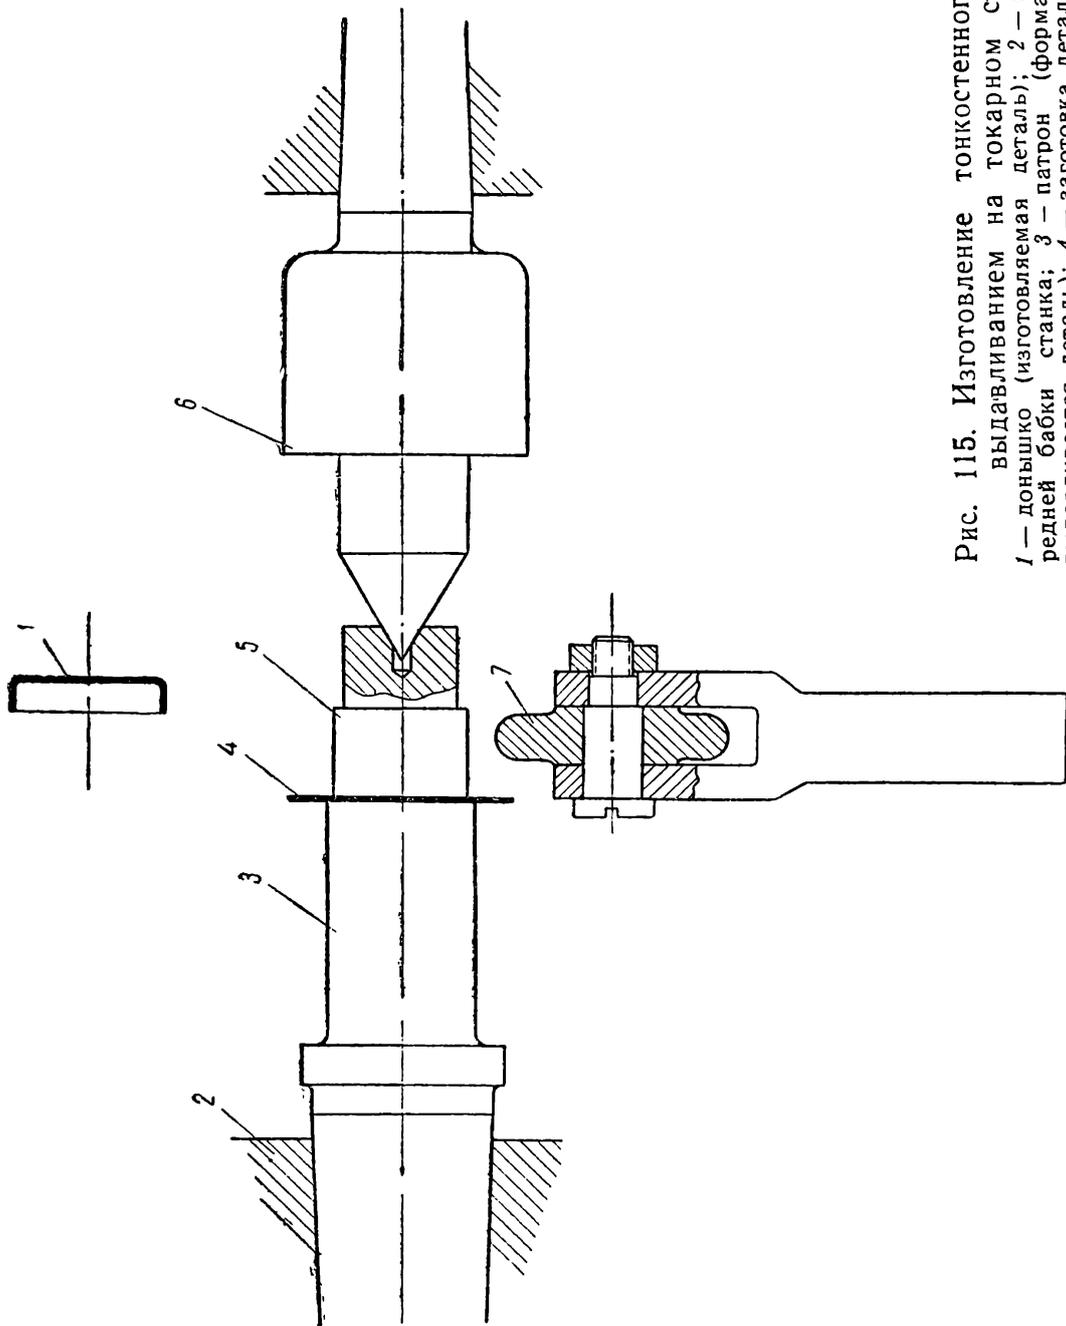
Изготовление тонкостенного доннышка выдавливанием на токарном станке:
